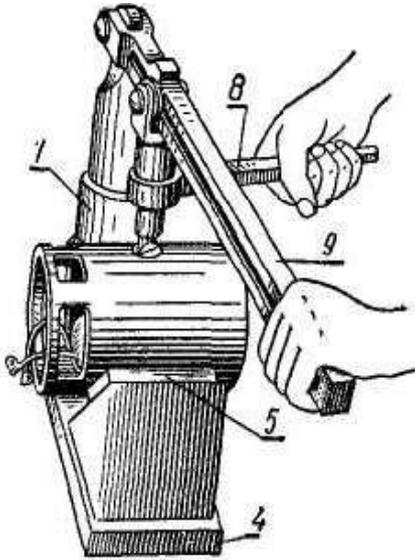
Рычажное устройство для вывертывания винтов
